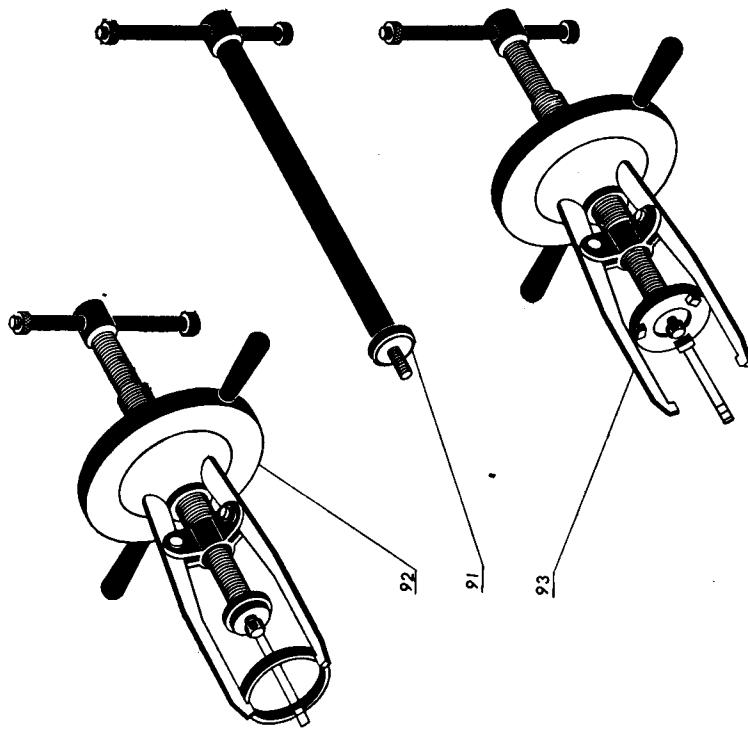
Привод регулятора и автомата пуска. Приспособления
